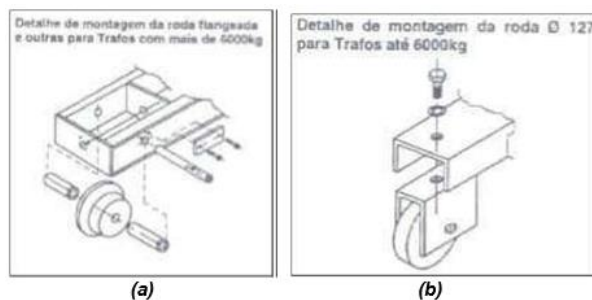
Exemplo de rodas; a) Flangeada; b) Lisa
